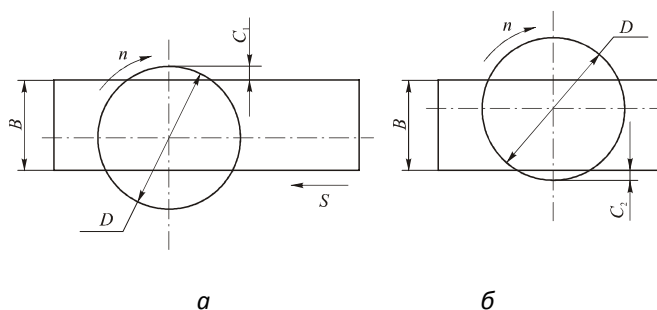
Расположение заготовки при торцовом фрезеровании относительно фрезы: *а* – врезание зуба фрезы при $c_1 = (0,03 \dots 0,05) D$; *б* – выход зуба фрезы при $c_2 = (0,03 \dots 0,05) D$.
